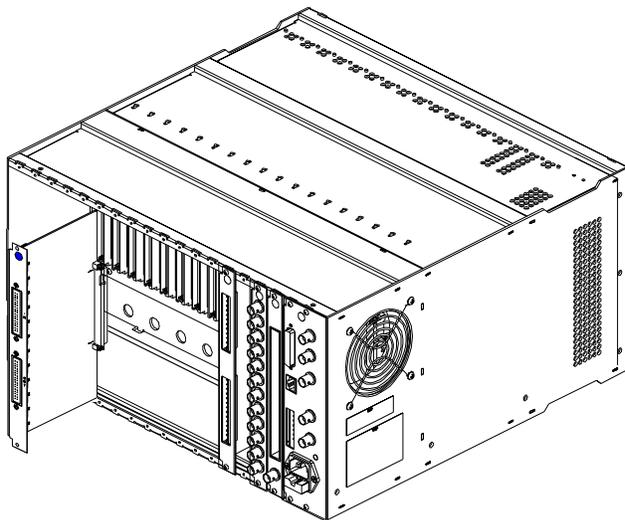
A - Ensemble du panneau arrière du module VIM-4 dans la baie
